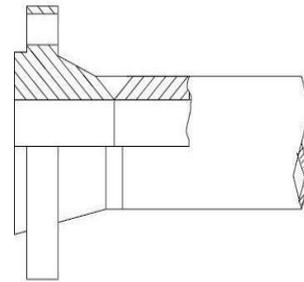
Diseño del bisel en la junta de soldadura para tubos de diferente espesor de pared
